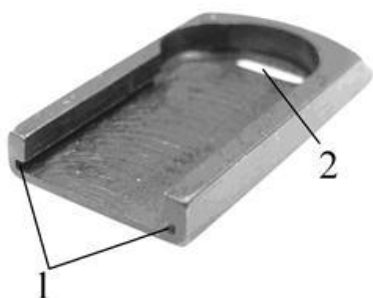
Крышка магазина: 1 пазы; 2 отверстие
